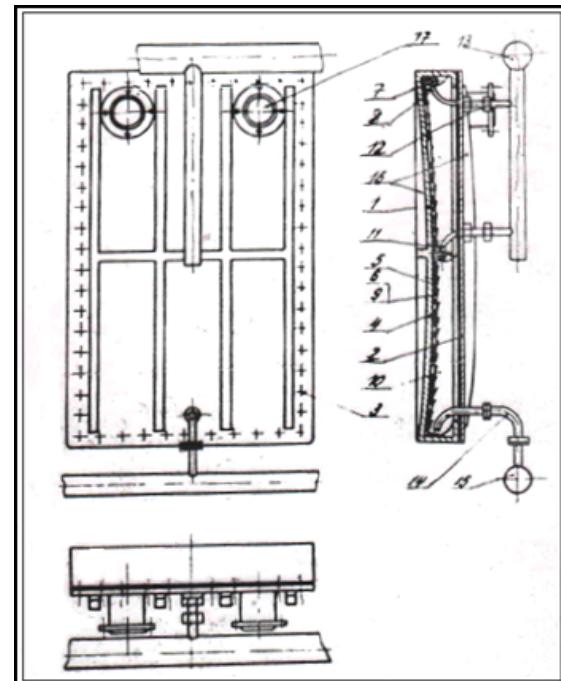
Конструктивное выполнение кессона с капиллярно-пористой системой с внешним оребрением: 1 – корпус; 2 – крышка; 3 – болт; 4 – стенка; 5 – капиллярно-пористая структура; 6 – пластина; 7 – артерия; 8 – корытце; 9 – отверстие; 10 – канал; 11, 17 – патрубок; 12 – труба; 13, 15 – коллектор; 14 – сифон; 16 – внешнее оребрение
